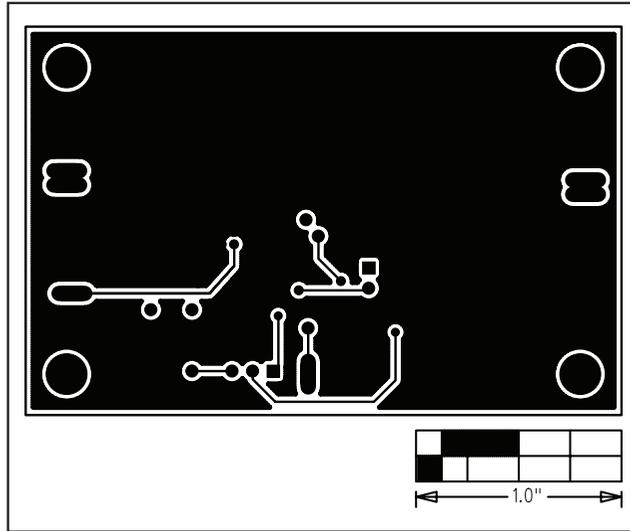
MAX4211E 评估板 PCB 布局 — 焊接层
